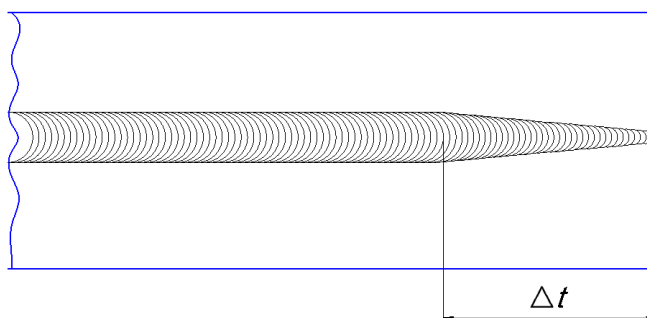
Эскиз сварного соединения при увеличении скорости сварки
